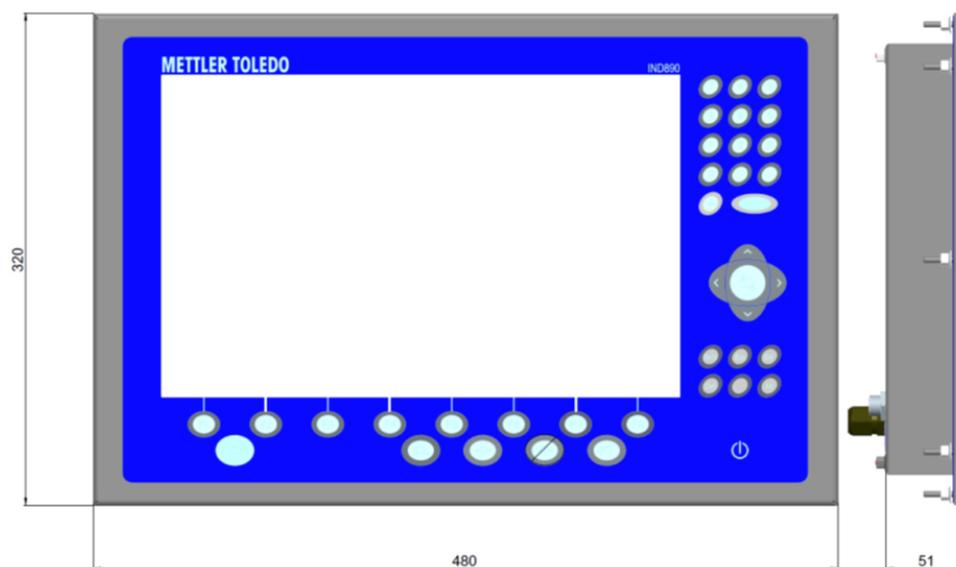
Dimensions IND970-15, Encastré dans panneau
